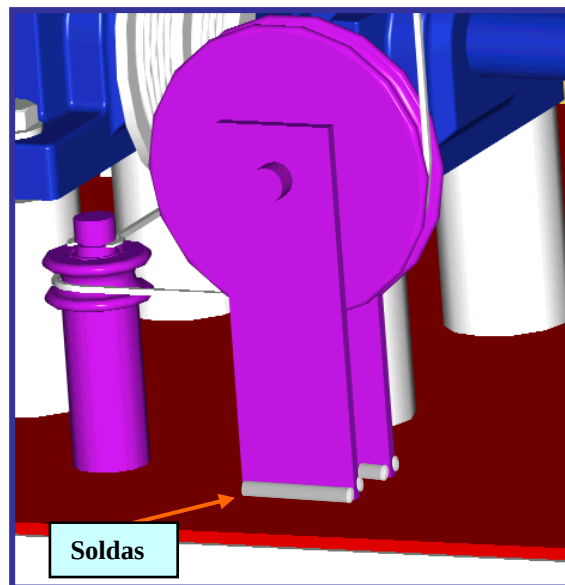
Filetes de solda da base do pedestal da roldana maior da Base.
